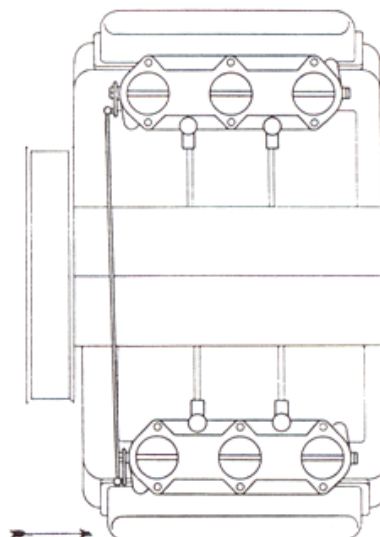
Utilización de carburadores de triple cuerpo en un motor de seis cilindros de tipo boxer.
